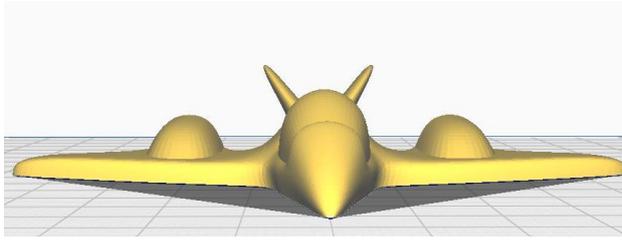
Frontansicht Testobjekt 1 - Mini-Flugzeug
